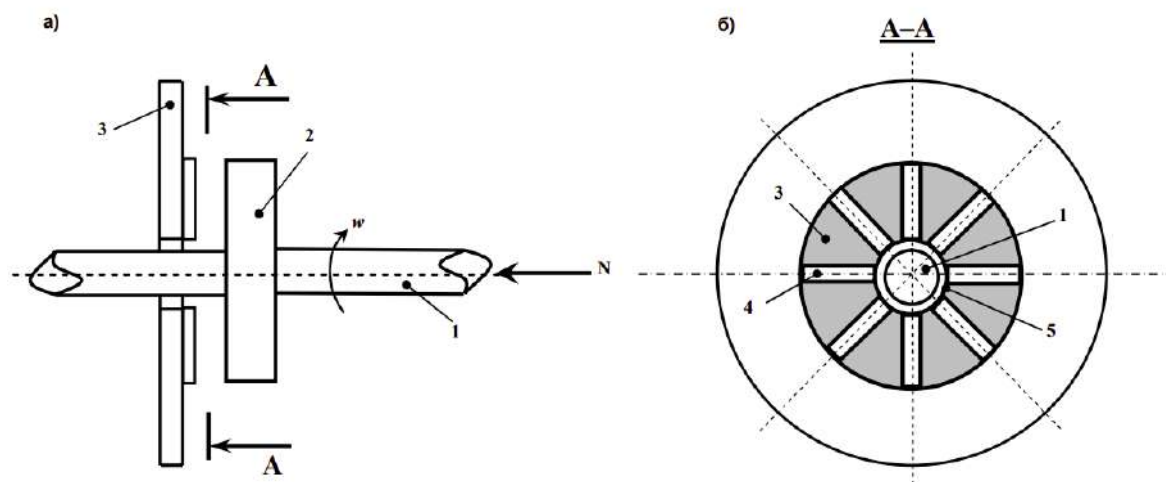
Схема упорного гідродинамічного підшипника (а) – вид збоку; б) – розріз АА): 1 – ротор; 2 – п'ята; 3 – УП; 4 – осьова канавка; 5 – кільцева канавка
